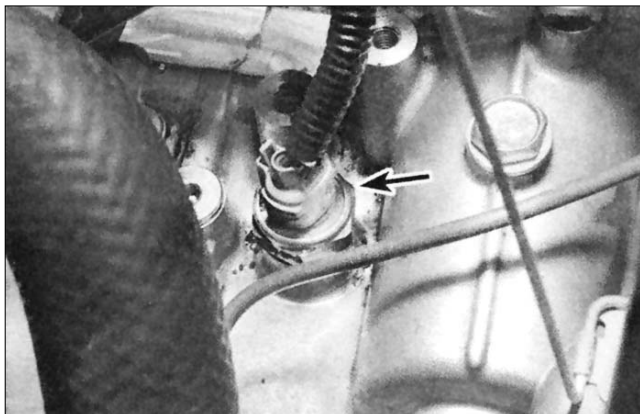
Выключатель фонарей заднего хода вкручен в верхнюю часть корпуса коробки передач
